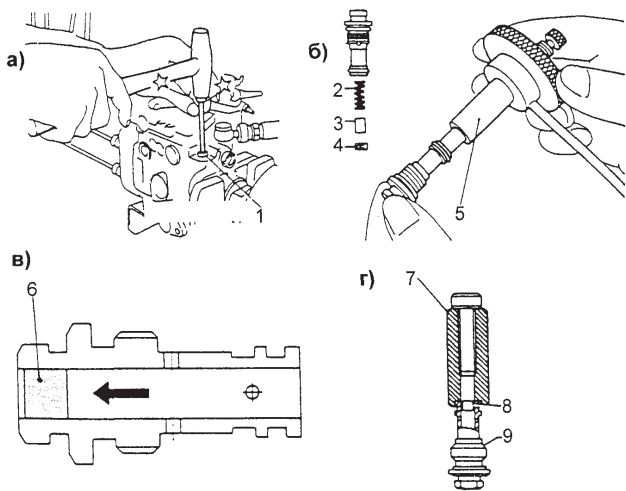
Регулировки перепускного клапана низкого давления: 1 - клапан, 2 - пружина, 3 - поршень, 4 - пружинное кольцо, 5 - приспособление (7 на рис. 2.42), 6 - пробка-упор пружины, 7 - приспособление (8 на рис. 2.42), 8 - пружинное кольцо, 9 - перепускной клапан.
